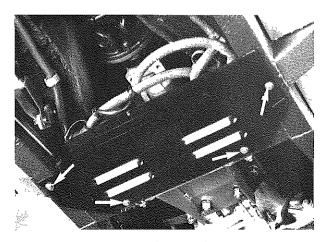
Smontaggio della paratia di protezione pompa Removing the pump protecting shield
